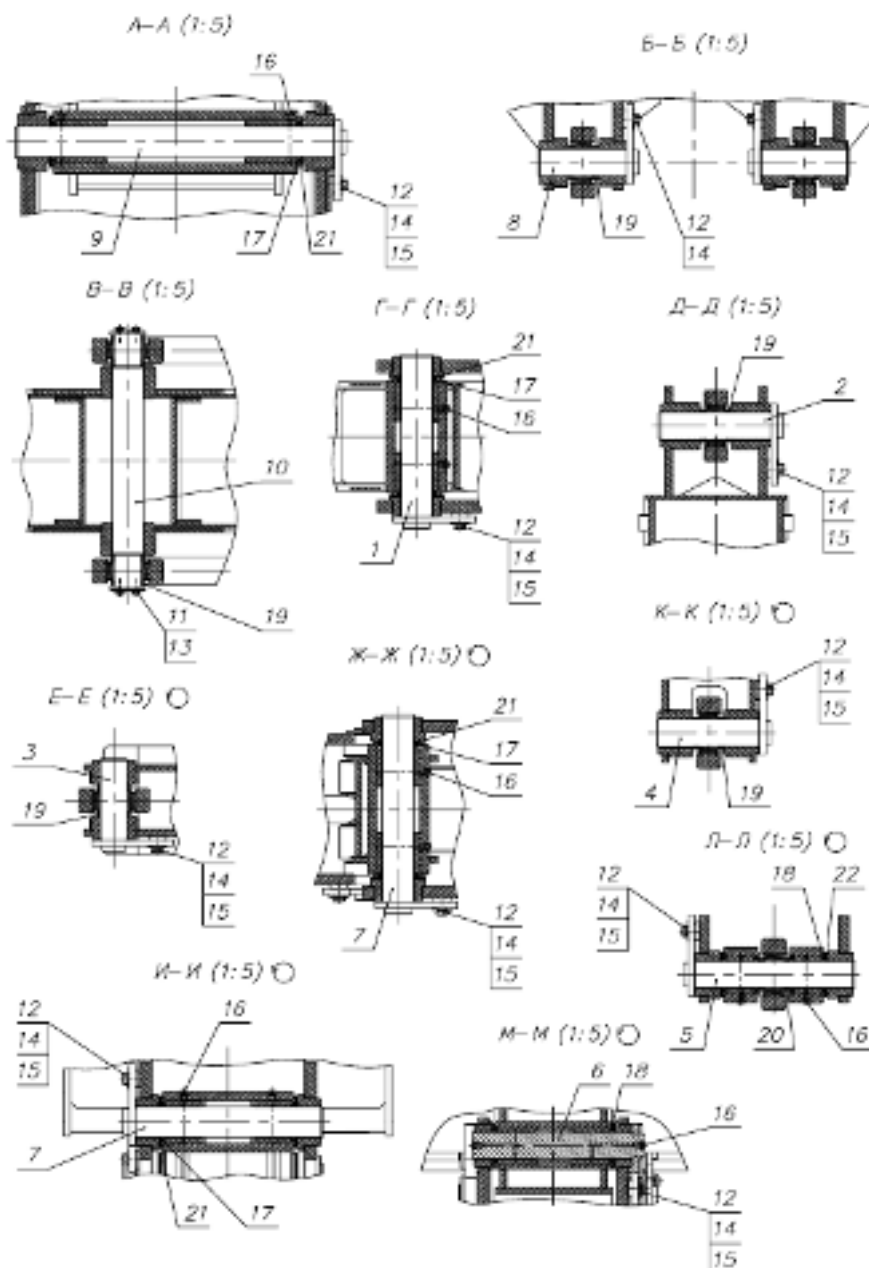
Шарниры рабочего оборудования обратная лопата
